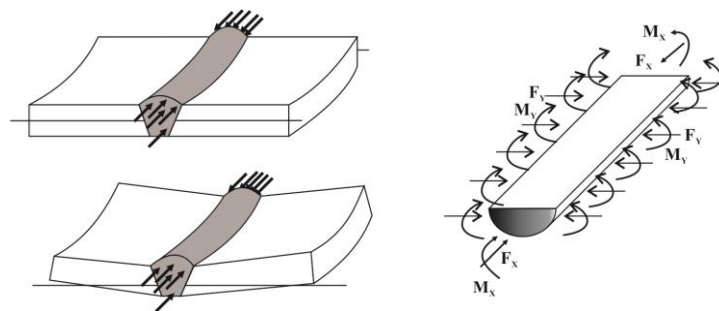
Deformações combinadas em uma placa soldada.
